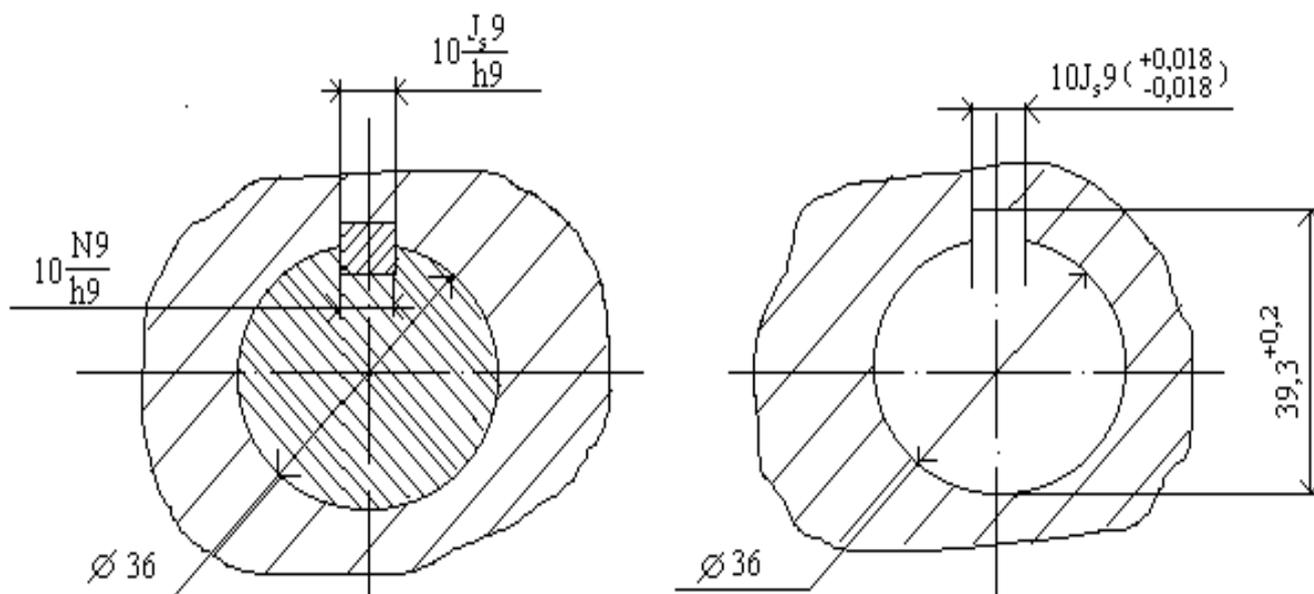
Эскизы деталей шпоночного соединения
